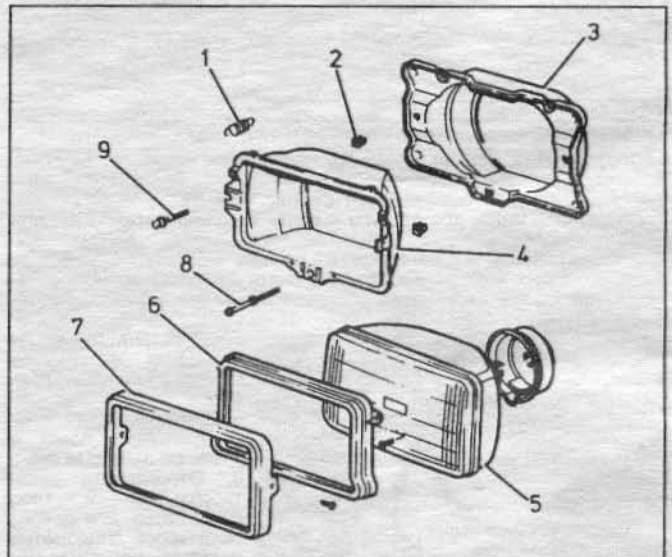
Сборка фары: 1 - пружина; 2 - пластиковая гайка; 3 - панель; 4 - держатель; 5 - блок-фара; 6 - удерживающее кольцо; 7 - накладка; 8 - винт вертикальной регулировки; 9 - винт горизонтальной регулировки.
